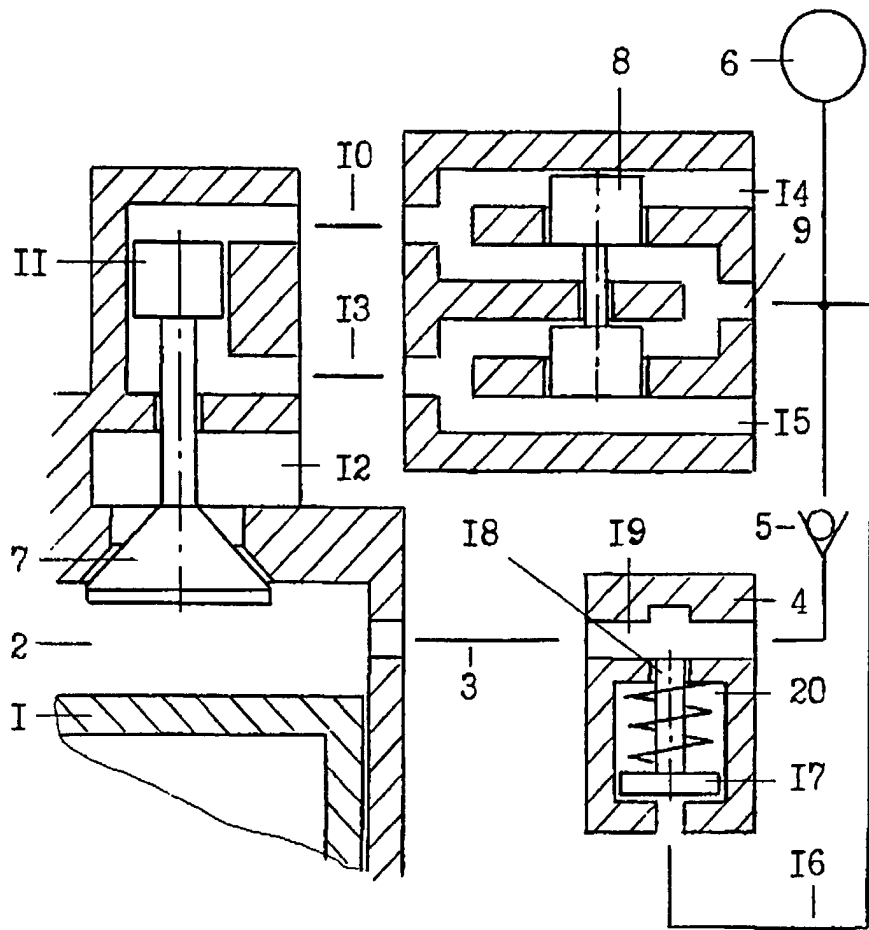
Схема привода компрессора зарядки гидроаккумулятора системы пневматического привода газораспределительного клапана и топливной форсунки двигателя внутреннего сгорания рабочим телом из цилиндра двигателя внутреннего сгорания.
